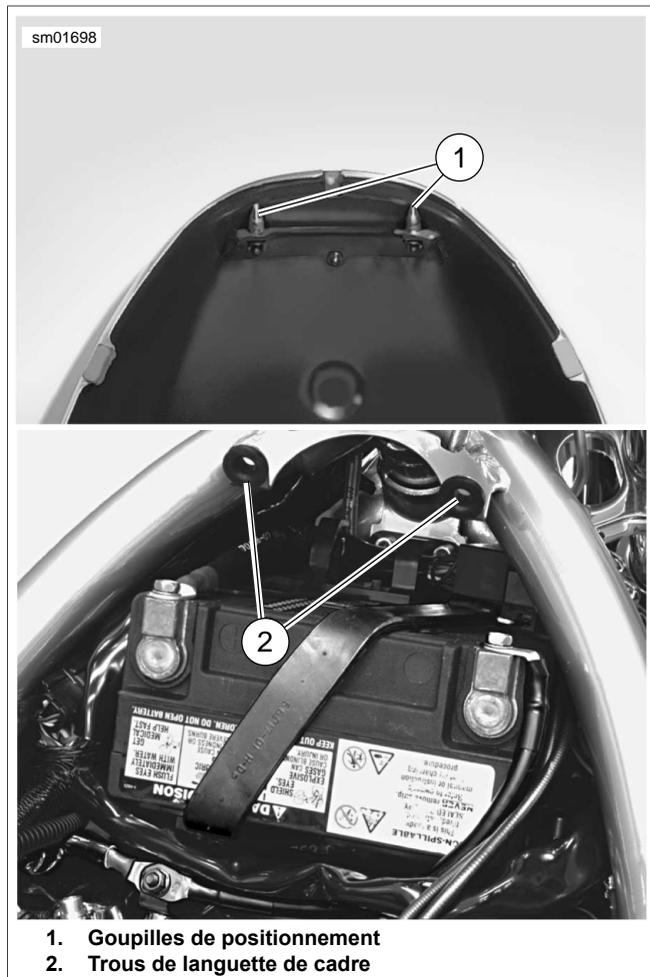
Couvercle de boîte à air et languettes de cadre (typiques)
